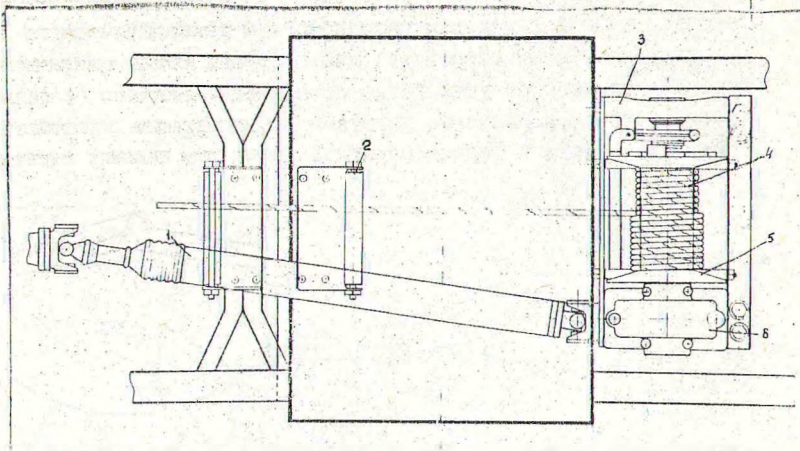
Установка лебедки на лесовозном тягаче: 1 - карданный вал привода лебедки; 2 - ролик; 3 - траверса; 4 - трос; 5 - барабан; 6 - редуктор.
